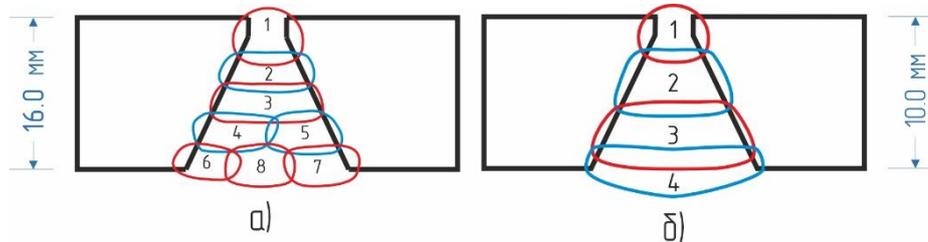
Очередность выполнения сварочных проходов: а) Для пластин толщиной 16мм.; б) для пластин толщиной 10 мм.
